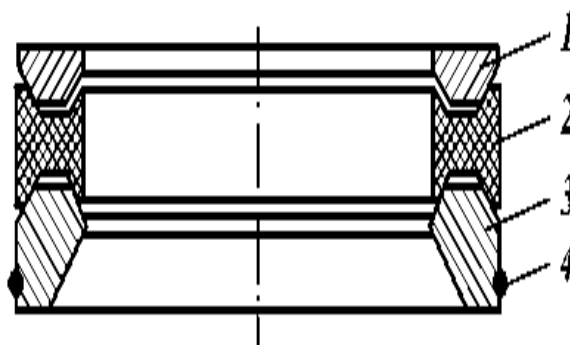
Пакерное устройство: 1- кольцо нажимное; 2- пакер; 3- крышка подвески; 4- кольцо уплотнительное
